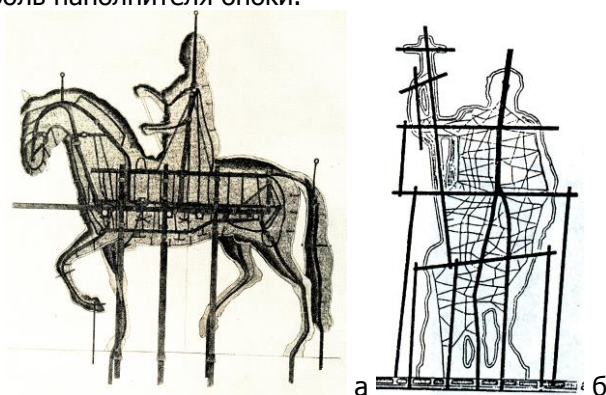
Металлический каркас стержня: а - Людовика XV [41]; б - князя Владимира [26]
